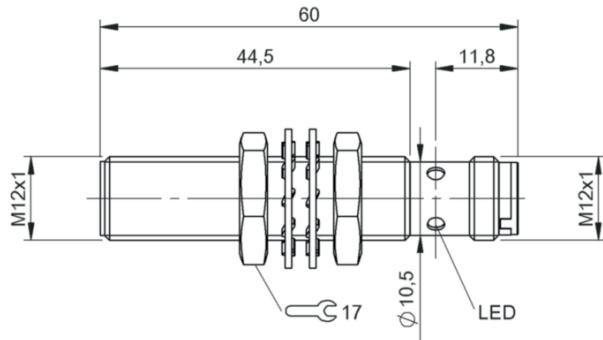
Aufbau Typen mit quasi bündigem Einbau
